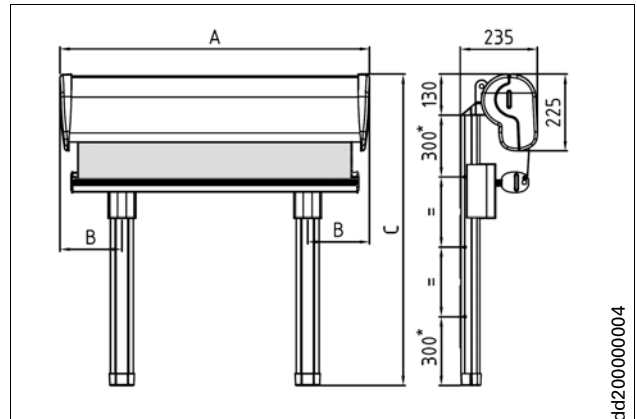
Maß-Skizze für Position Montageprofile (alle Maßangaben im mm)
